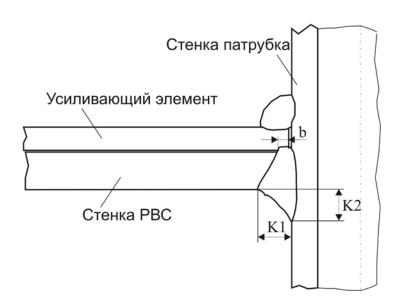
Схема сварного шва сопряжения патрубка со стенкой PBC
